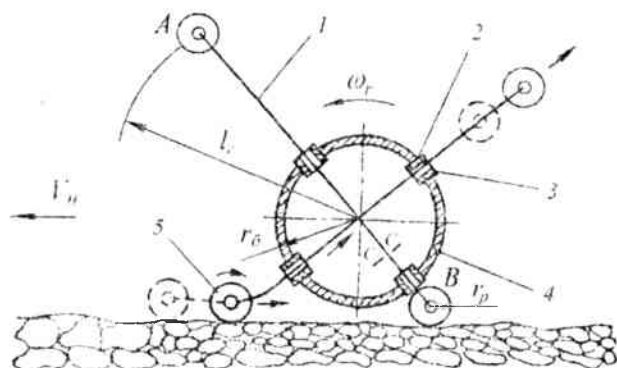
Ротационный рабочий орган с рабочими элементами на гибких держателях: 1 – гибкий держатель; 2 – отверстия; 3 – направляющая втулка; 4 – барабан; 5 – рабочие элементы
